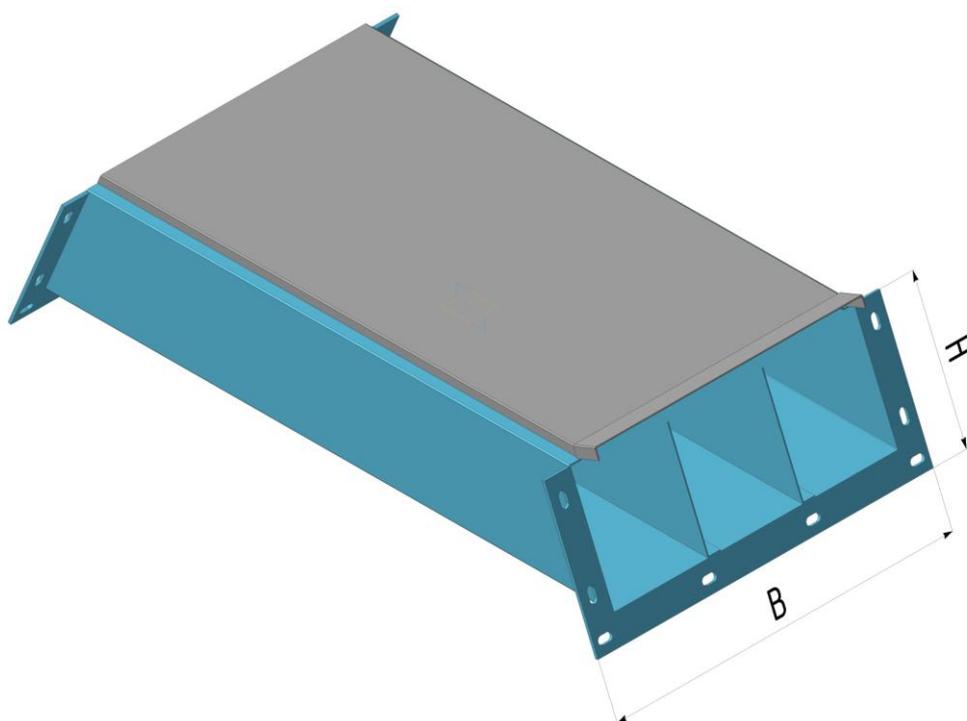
Короб кабельный блочный с поворотом вверх плоский типа ККБ-УВП. Общий вид
